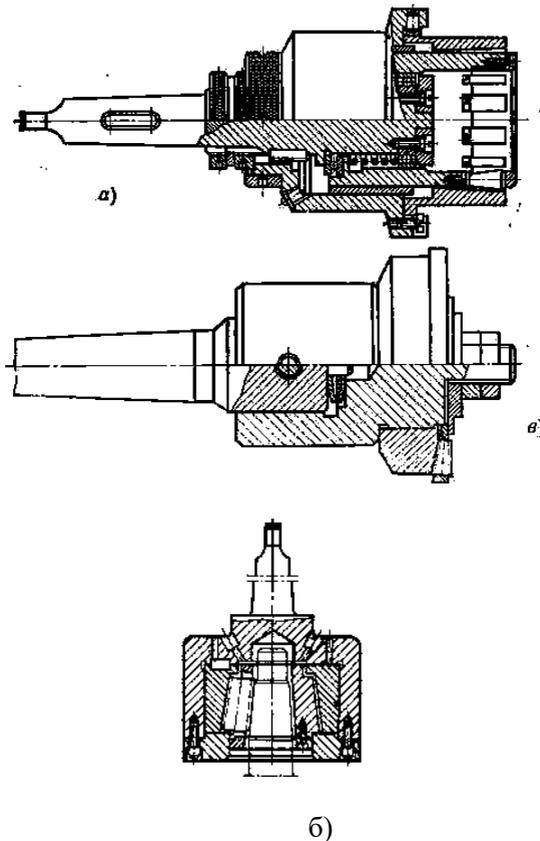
Багатороликові обкатки для обробки зовнішніх поверхонь:
